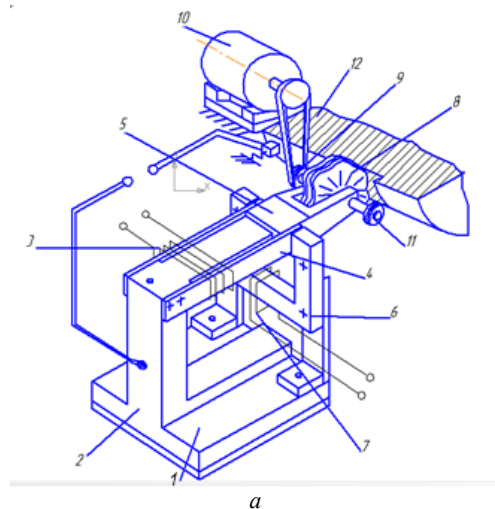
Схема установки для МАО поверхностей поршня:
